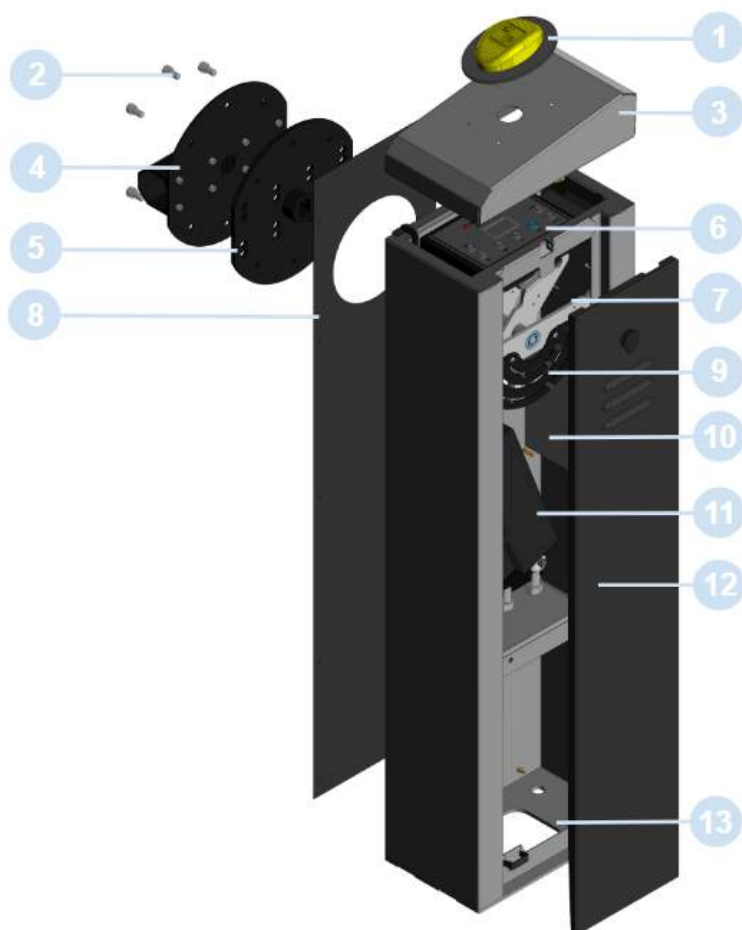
Внешний вид и состав корпуса шлагбаума
